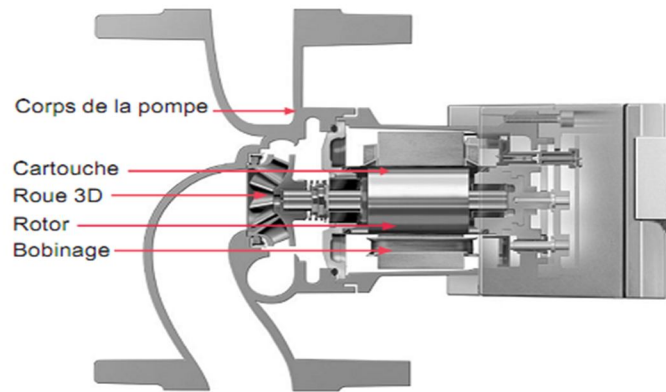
Coupe d'une pompe à rotor noyé [46].
